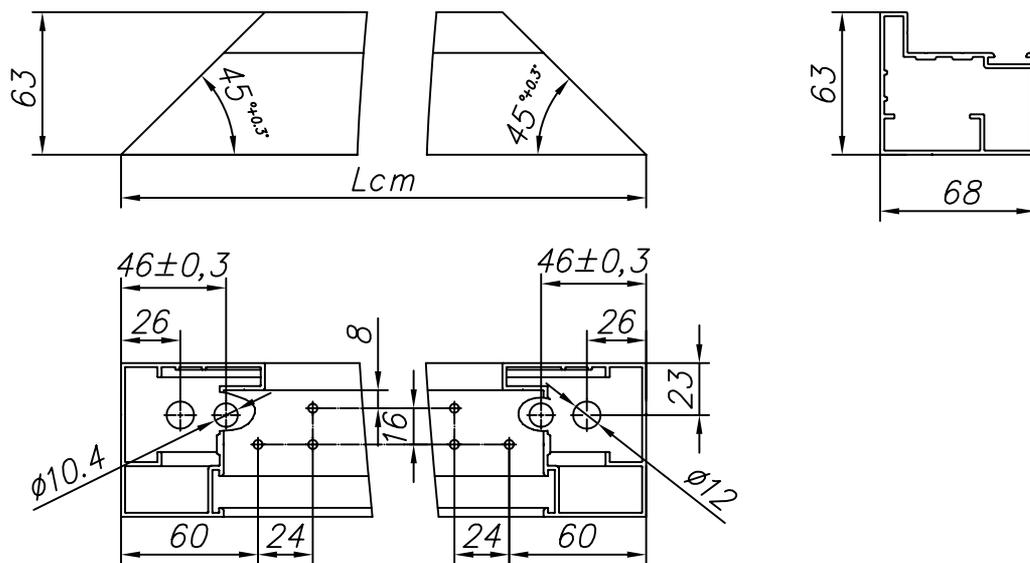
Изготовление стойки (профиль рамы FLGU.400.0107)
